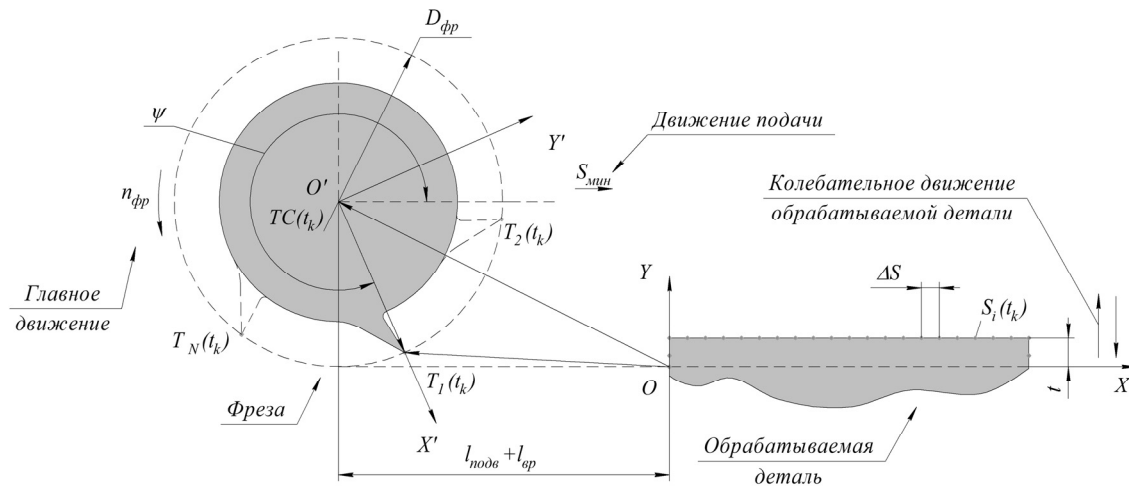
Геометрические модели фрезы и обрабатываемой детали
